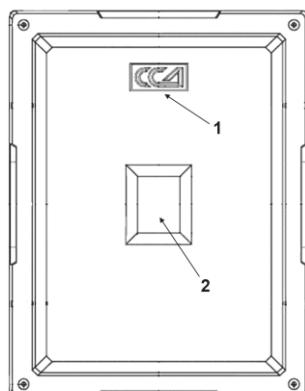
Вид сверху на корпус колодца «ККСр-1-10(80)»:
